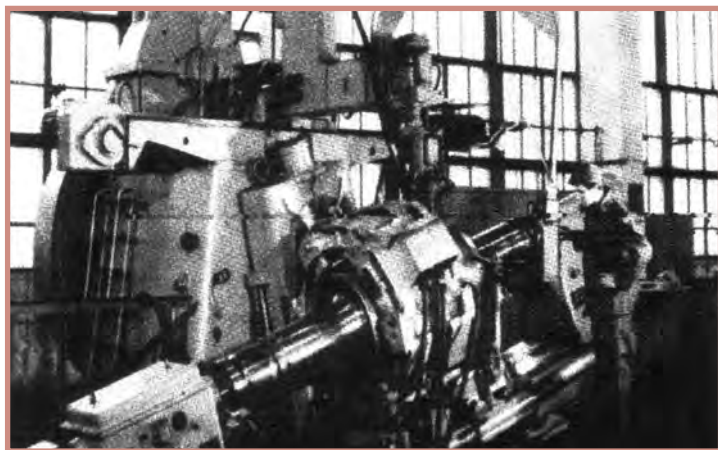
Наплавка вала сортопрокатного стана на вальценаплавочном станке КЖ–9711
